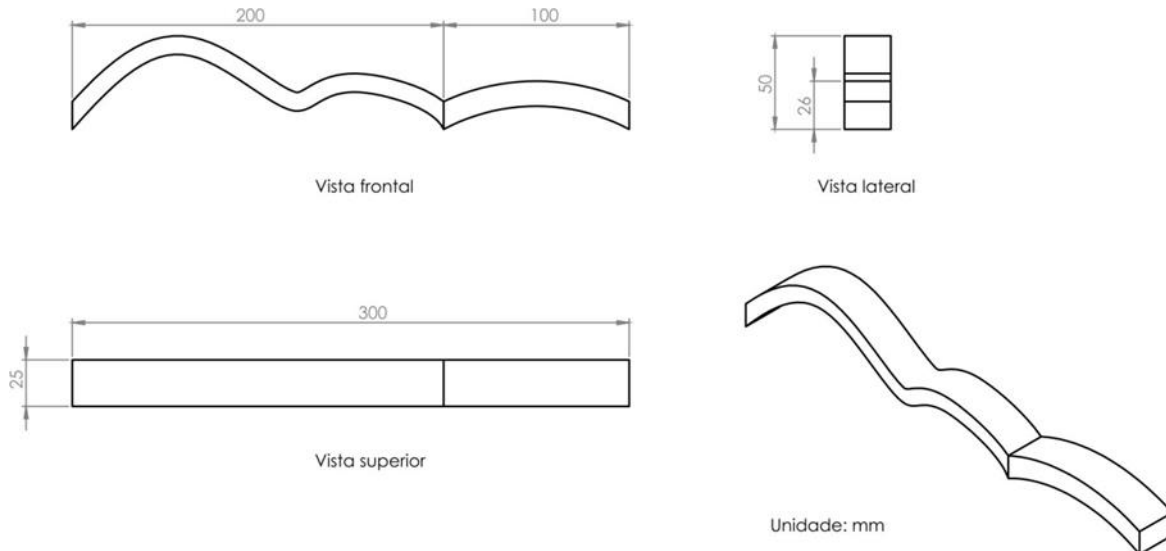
Desenho técnico com as dimensões gerais do multimódulo 1.
